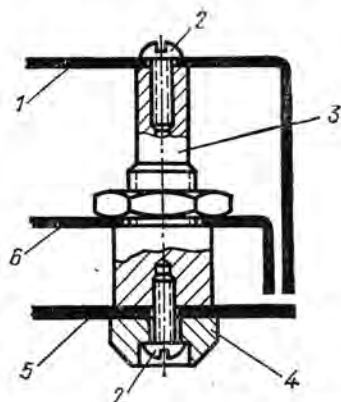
Способ скрепления панелей корпуса и шасси: 1 — верхняя панель; 2 — винты М2,5×6; 3 — стойка, сталь Ст 3, цинковать; 4 — ножка, сталь Ст 3, хромировать или воронить; 5 — нижняя панель; 6 — шасси.
